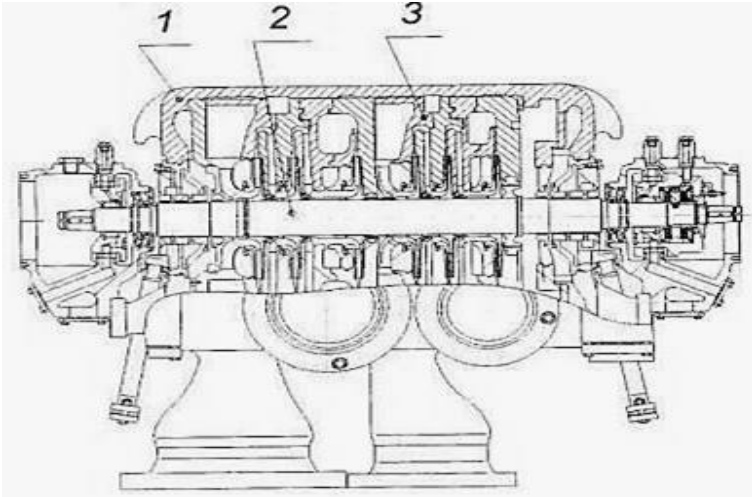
Базовий корпус із горизонтальним рознімом УВКМ другого покоління:
